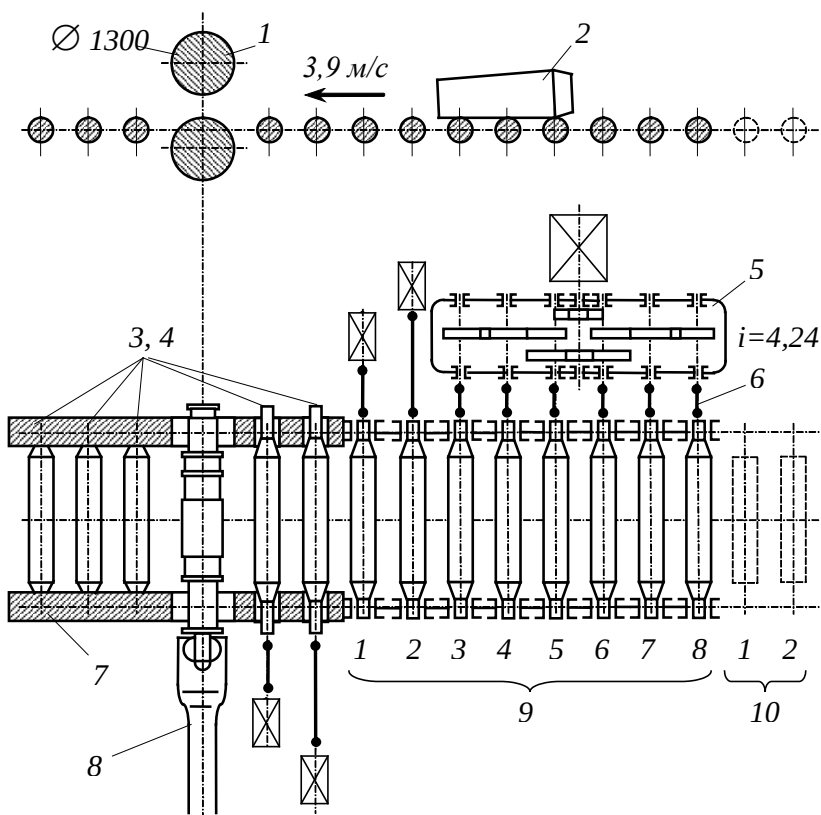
Рабочий рольганг блюминга 1300 конструкции УЗТМ:
